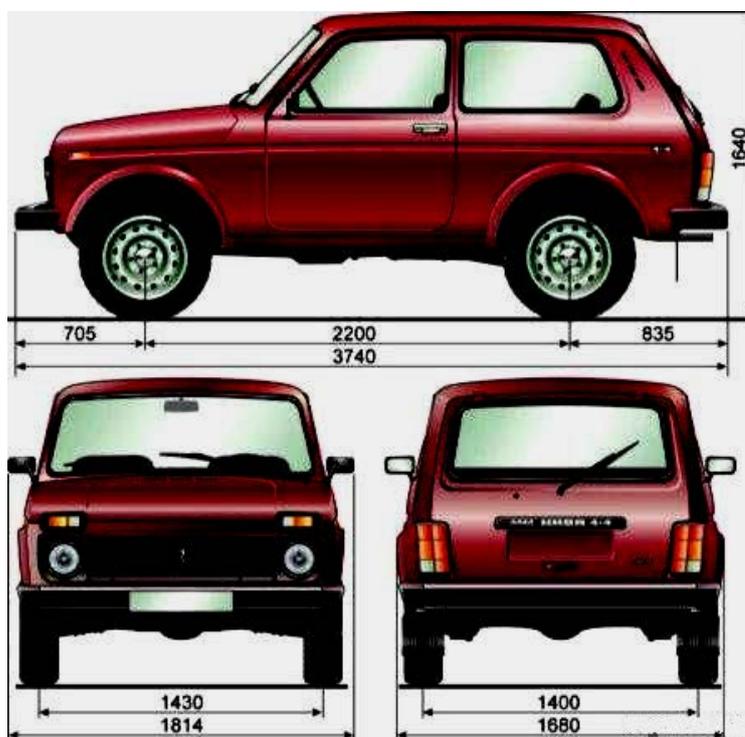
Габаритные размеры автомобиля ВАЗ 2121
